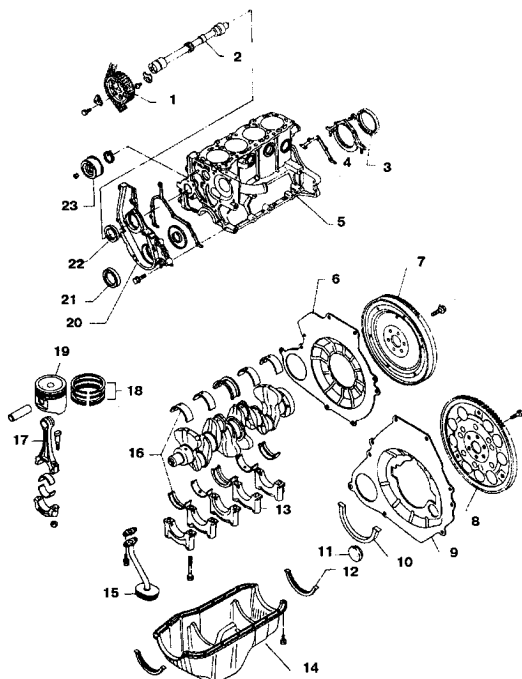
Элементы блока цилиндров (См. Раздел 9)
